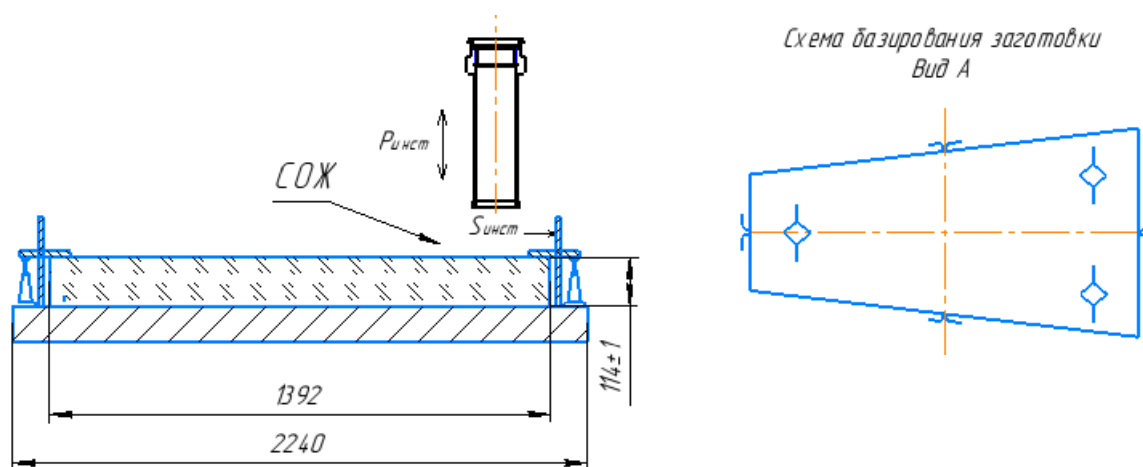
Эскиз операции фрезерования на станке 2Е-470
